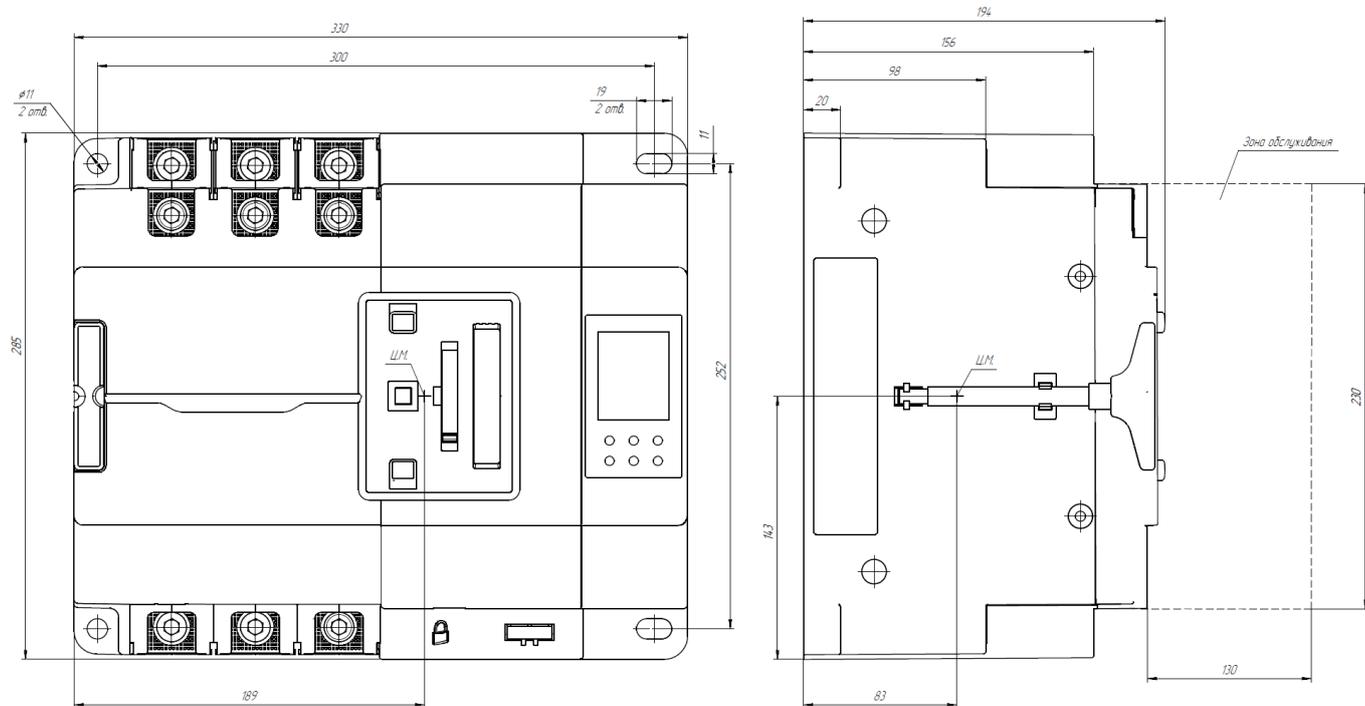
Габаритный чертеж OptiVerse SD 630 4P
